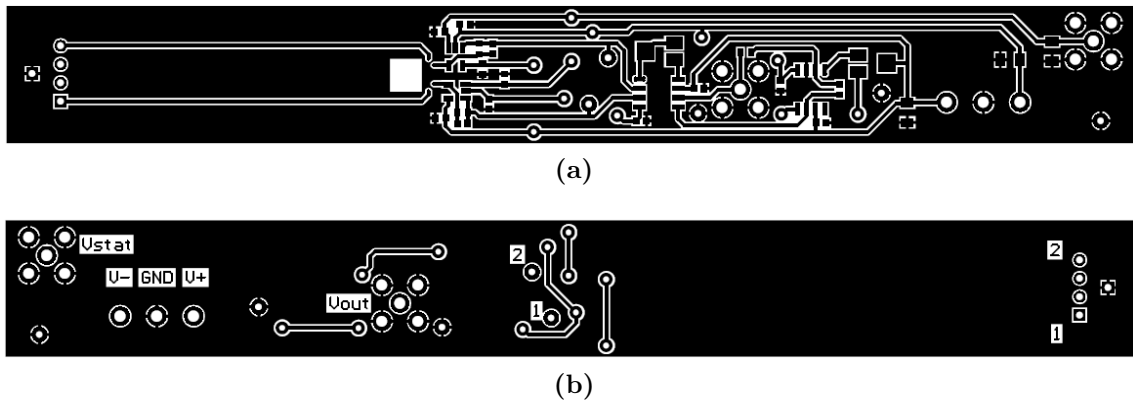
Layout per la stampa della PCB (a) vista dal basso, (b) vista dall'alto
